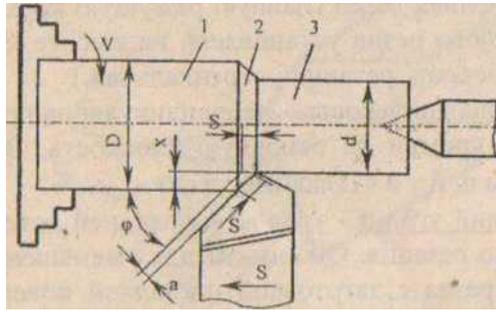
Поверхности на обрабатываемой заготовке и режимы резания при точении: 1 - обрабатываемая поверхность; 2 - поверхность резания; 3 - обработанная поверхность
